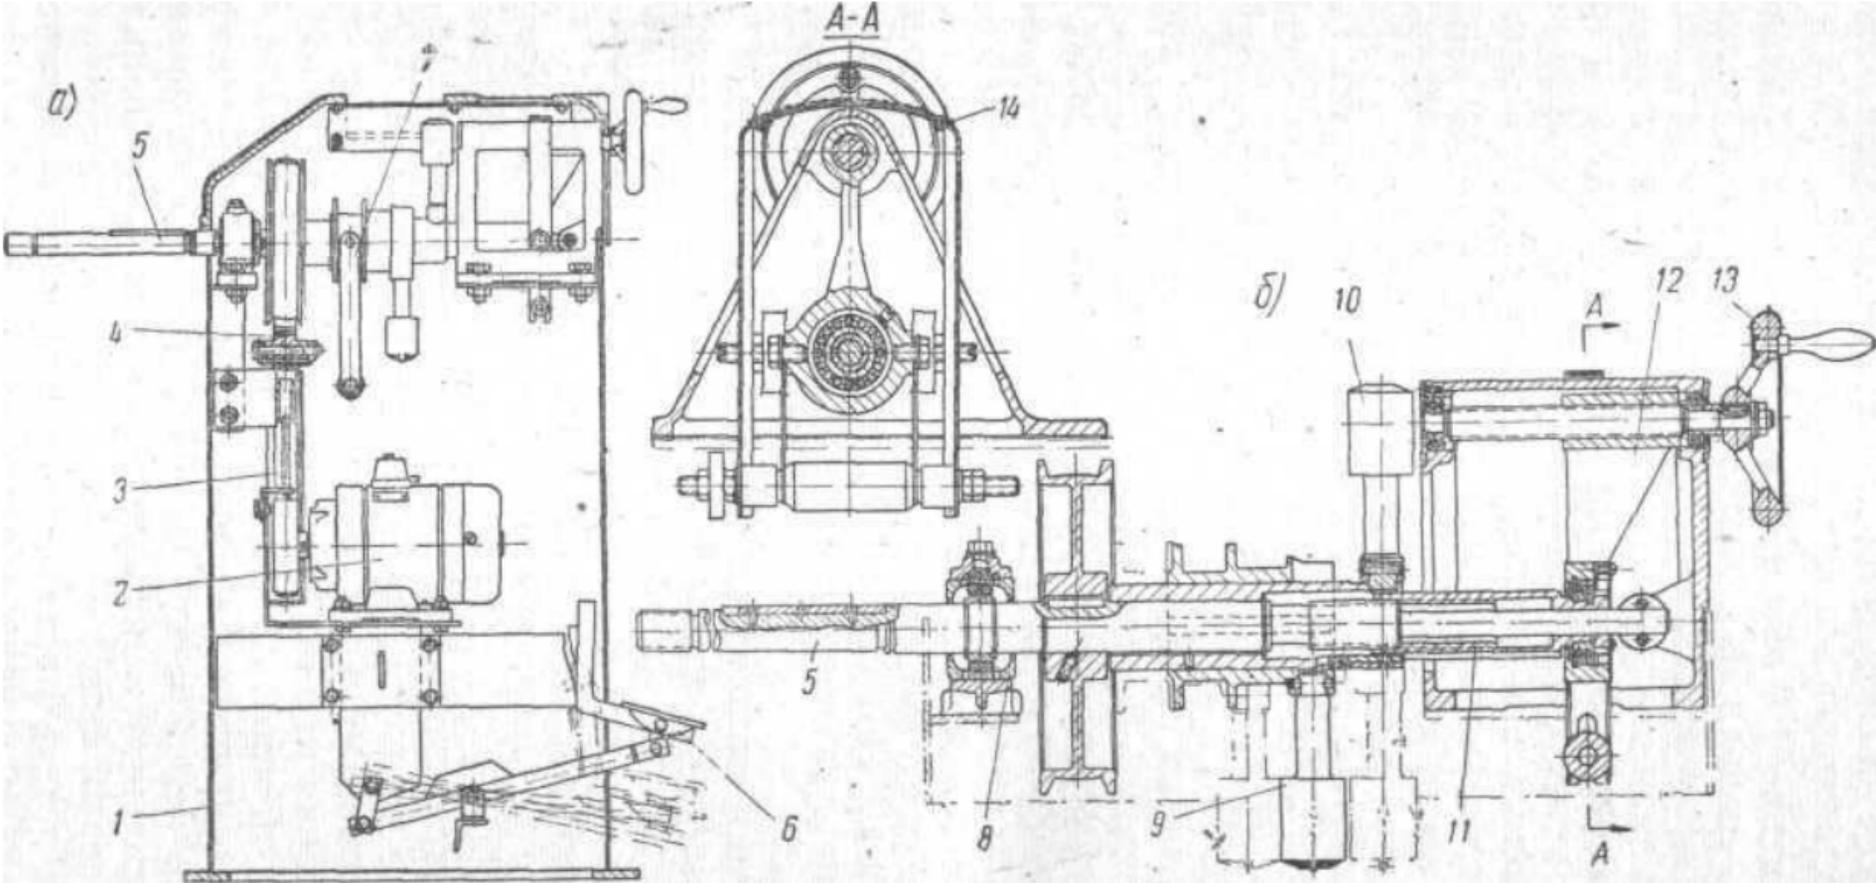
Станок для статической балансировки колес в сборе с шинами:
